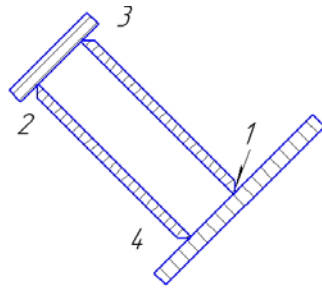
Положение заготовки при сварки шва №1
